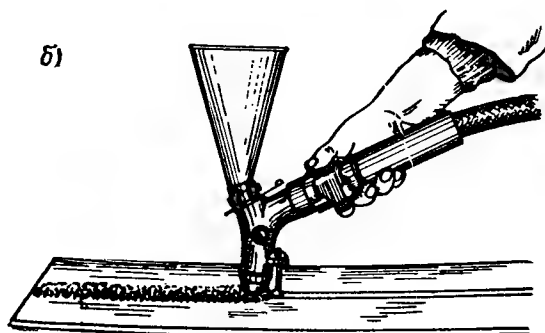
Полуавтомат ПШ-54 для сварки под флюсом Института электросварки им. Е. О. Патона
